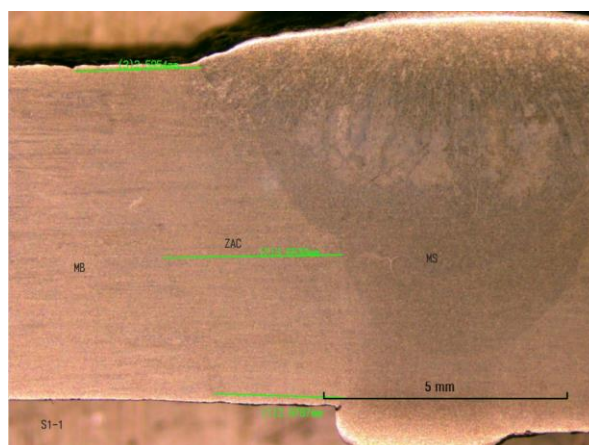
Medición de la ZAC para las juntas soldadas. WPS S\_01, probeta 1.
